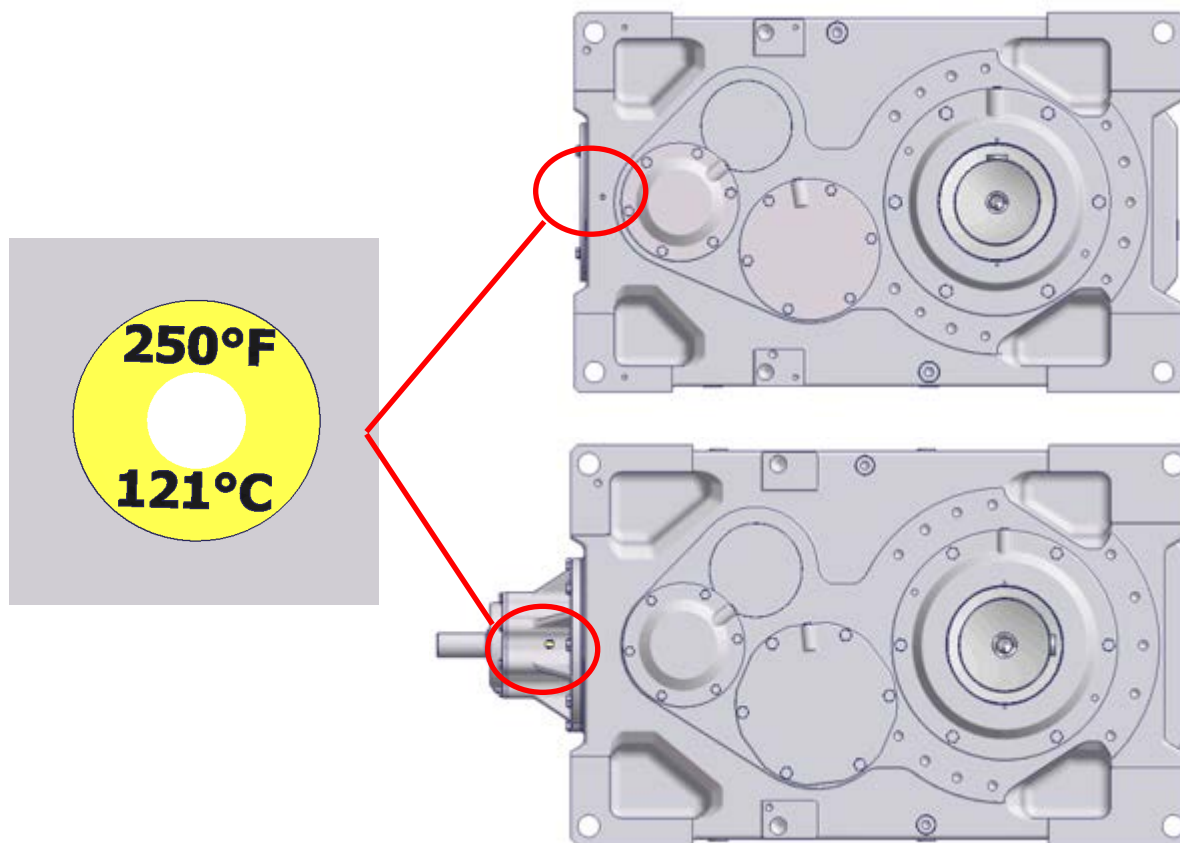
Положение наклейки-индикатора температуры на корпусе цилиндрического или конического редуктора
